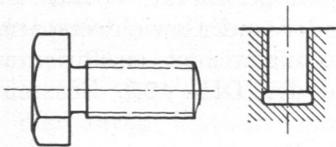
und 343. Schraube mit Rille, DIN 76, Gewindeloch mit Hinterdrehung, DIN 2352.
